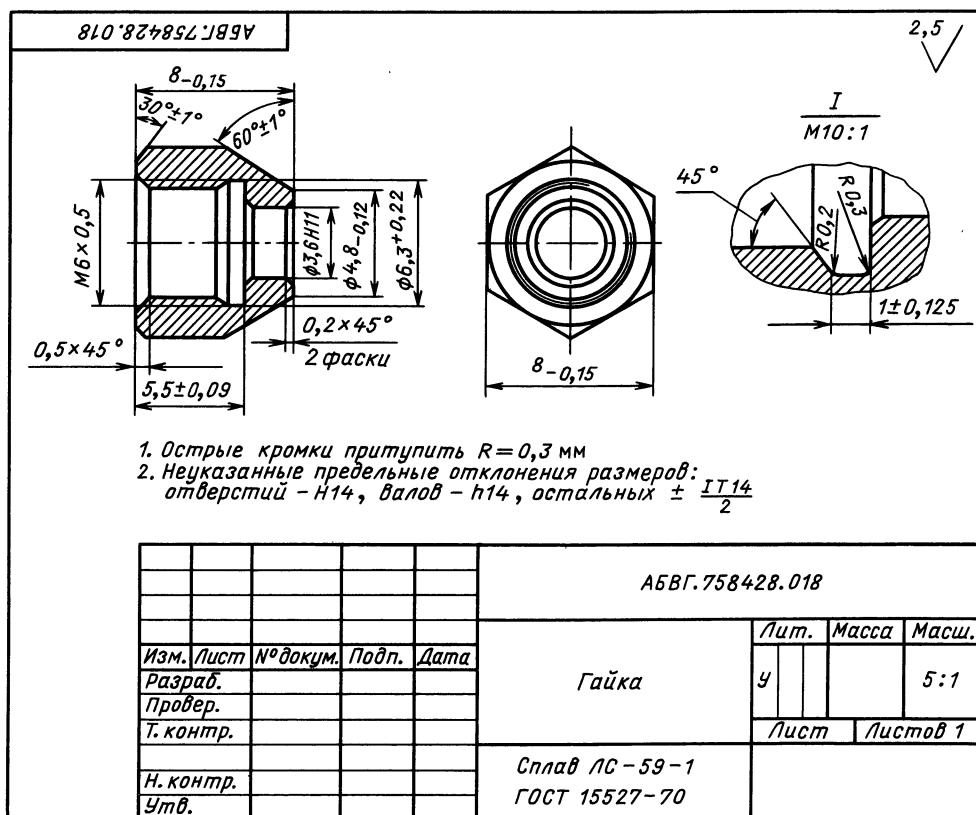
Конструкторский документ — чертеж детали «Гайка»
